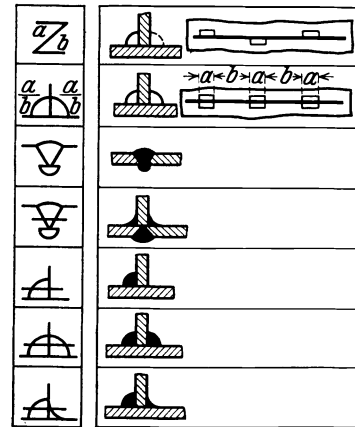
Kennzeichnung von Schweißverbindungen.
